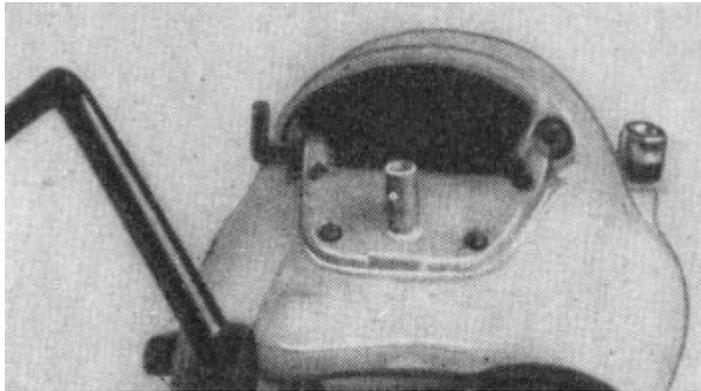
Starterklappe, Ausführung bis Motornummer 1601500
